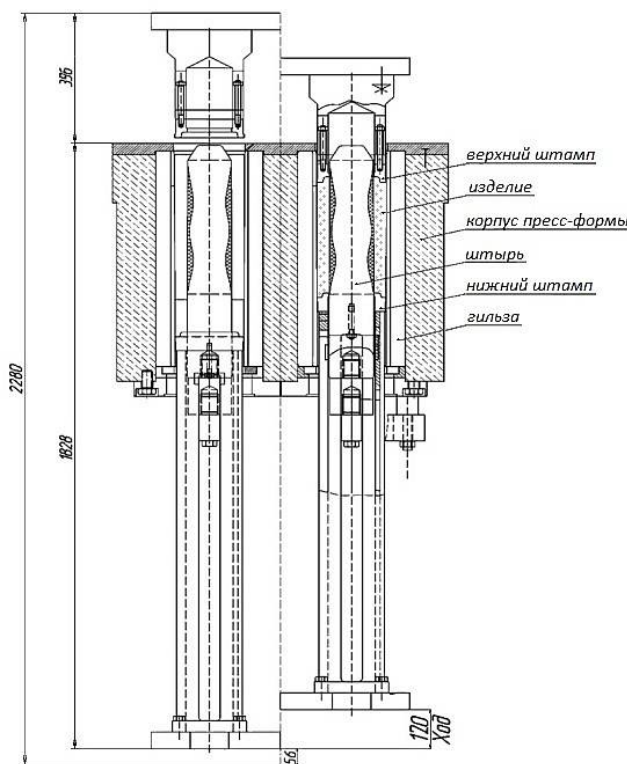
Схема ячейки пресс-формы для прессования полых цилиндрических изделий
